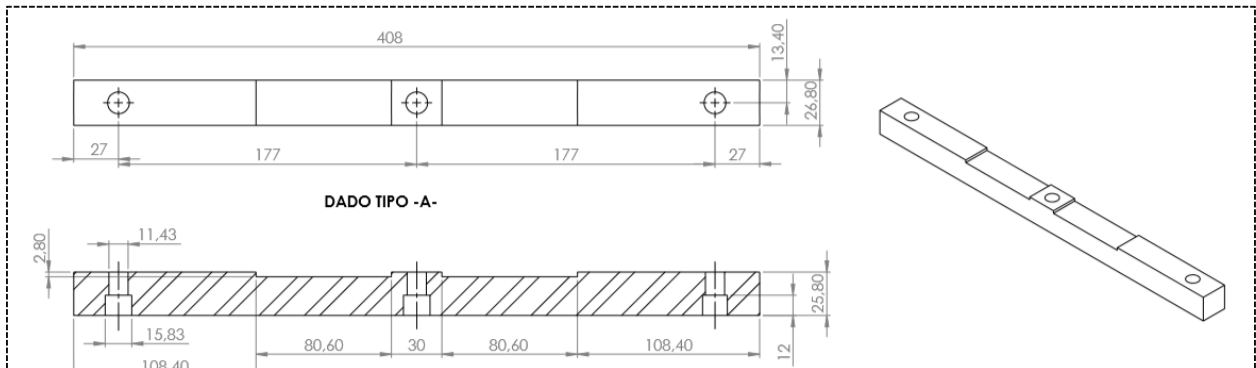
Planos dado tipo A. Fuente (Autores, Planos Dados, 2016)
